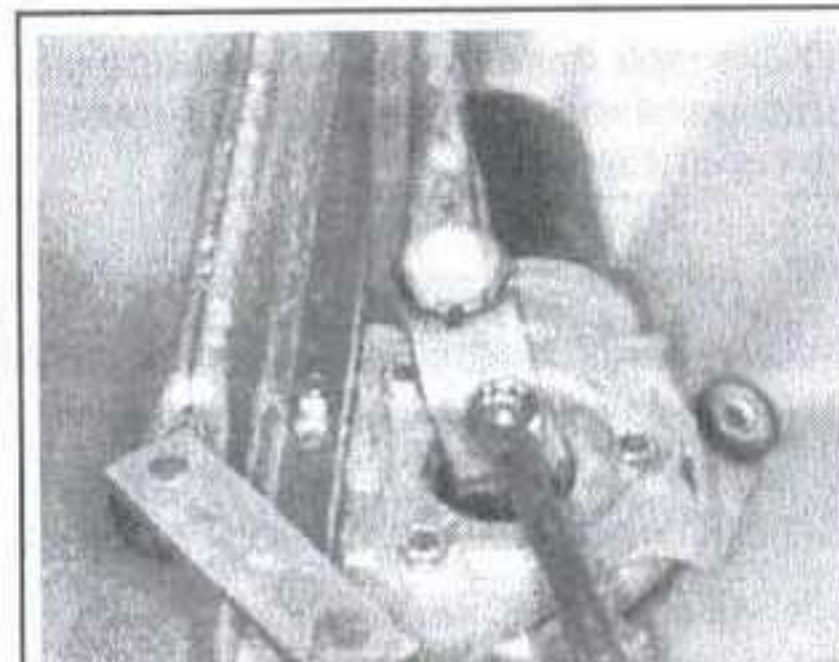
Открутите крепежную гайку шарнира очистителя с оси двигателя...
